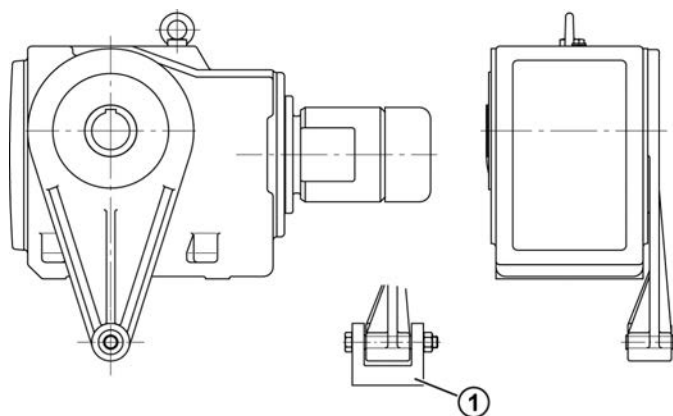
Montering af gummibufferne (option G eller VG) ved fladgear
